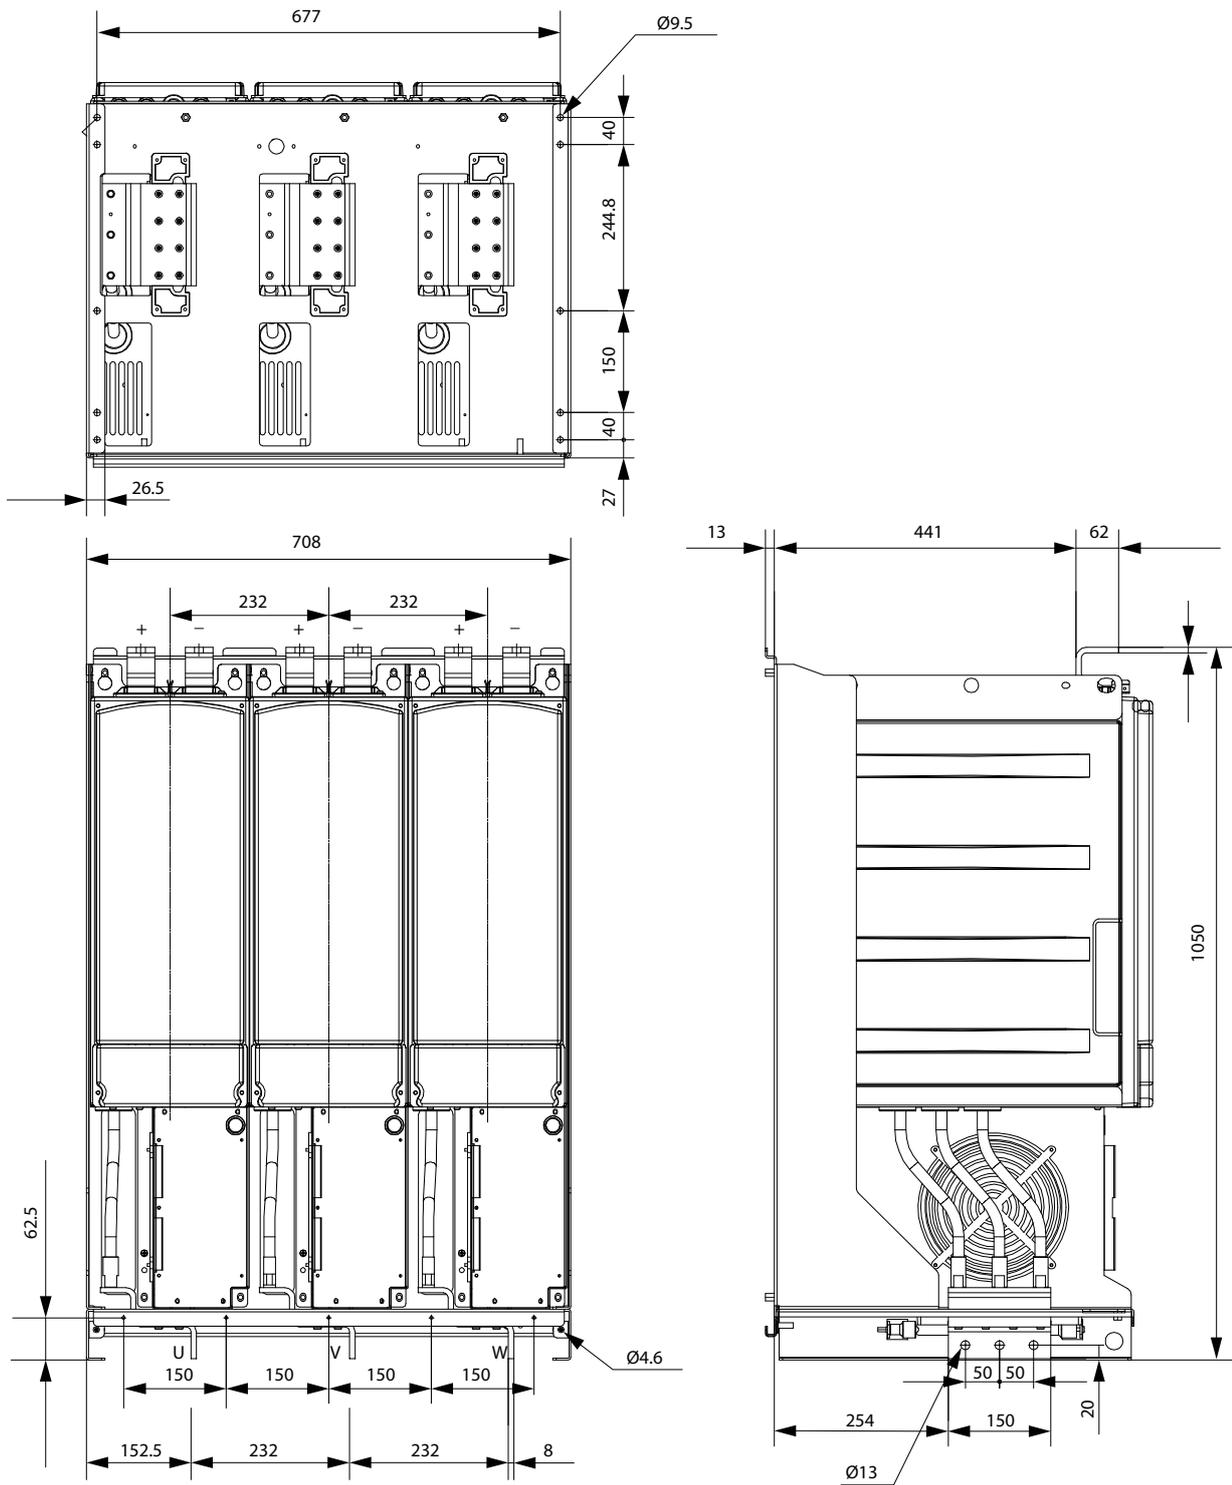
Dimensions du VACON® NX Inverter FI13, vue avant
